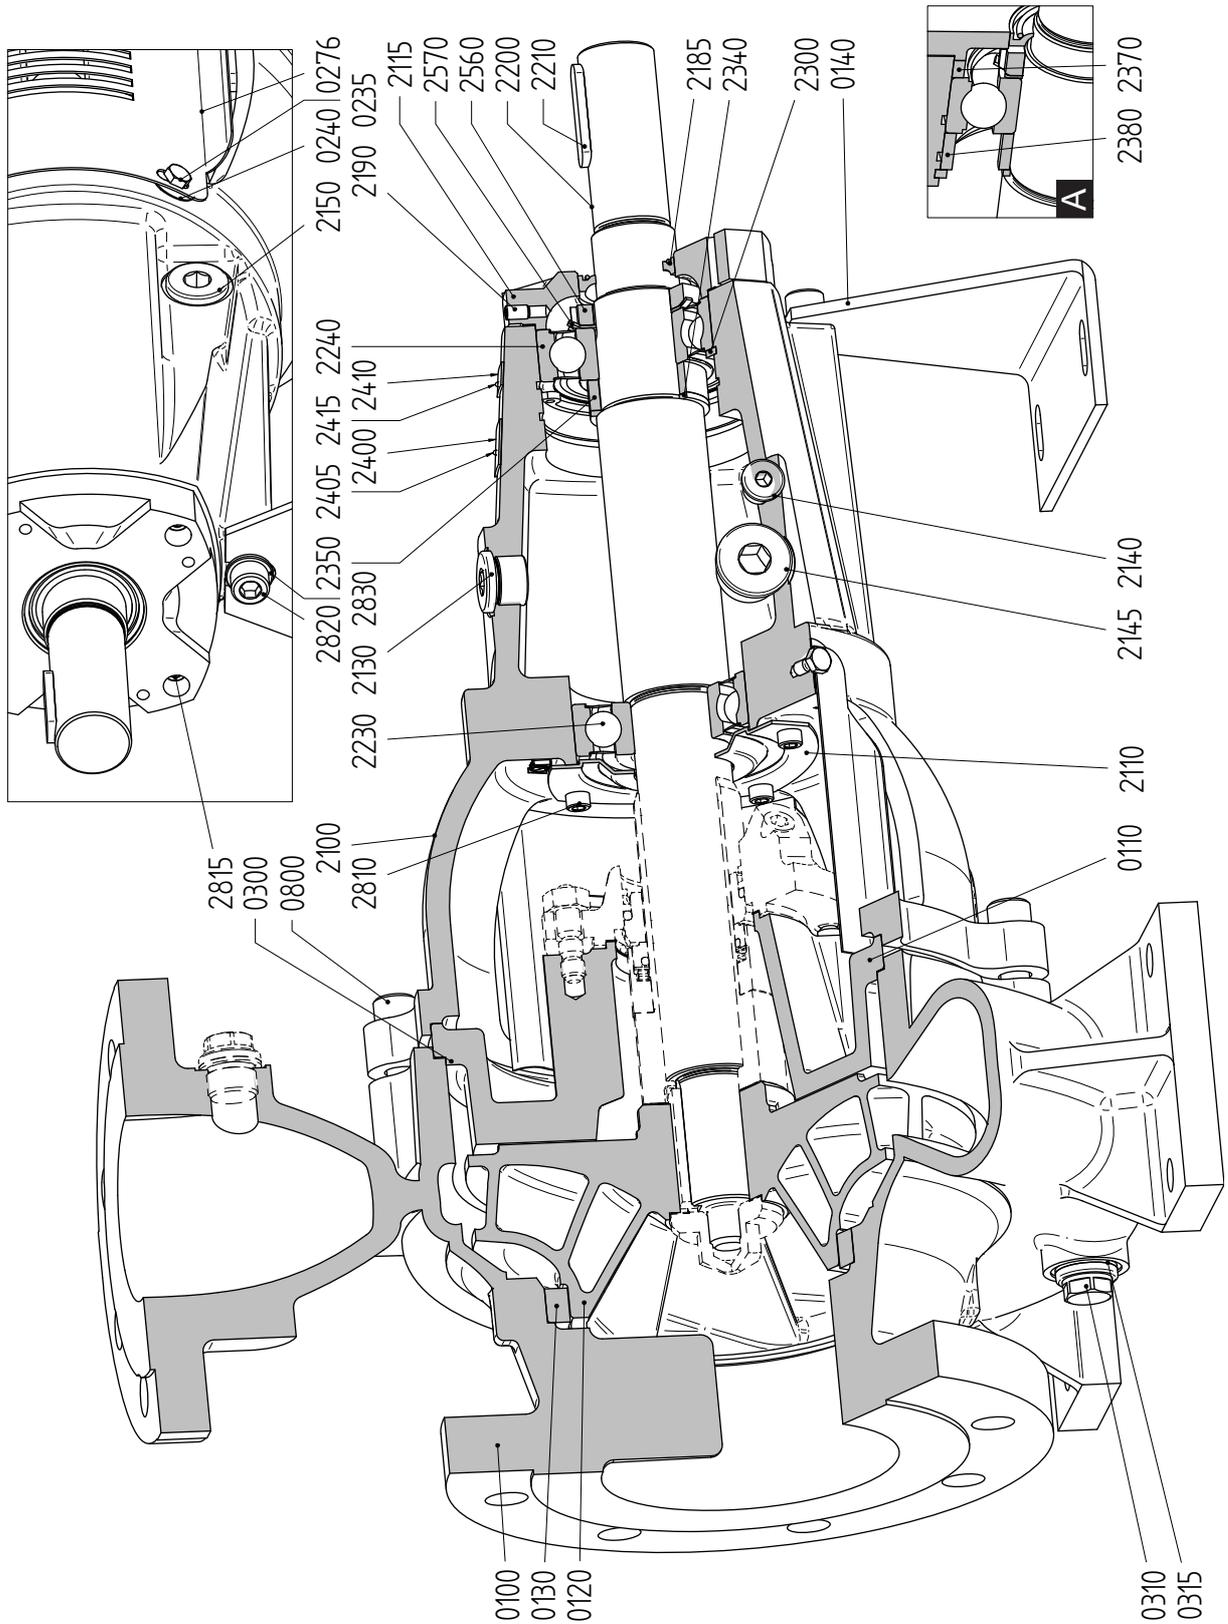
Чертеж в разрезе L1 с коническим отверстием (A = для группы подшипников 3)
